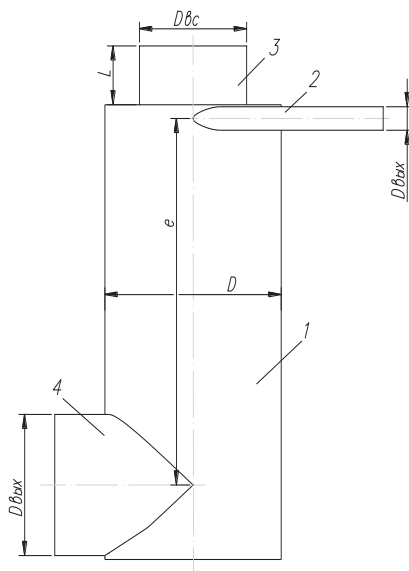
Схема вихревого эжектора. 1 - цилиндрический корпус аппарата;
